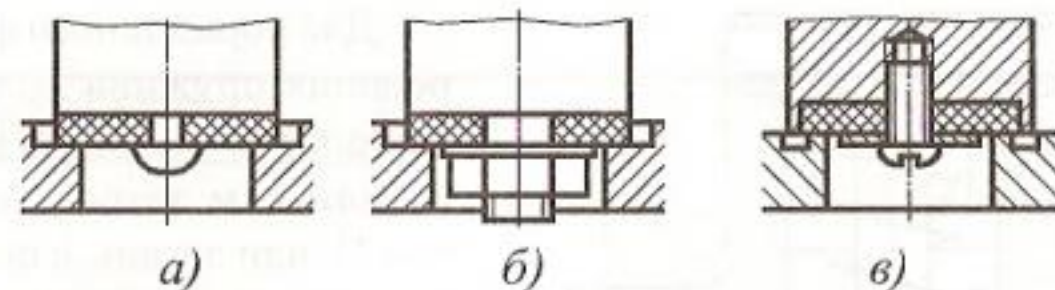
Примеры конструкций запорных пар для ПГА общего назначения
